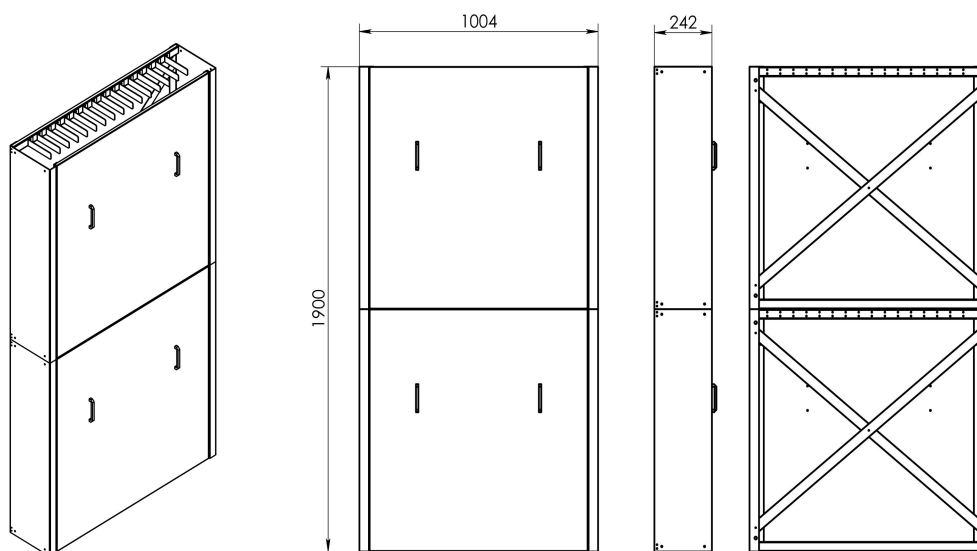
Габаритные размеры шкафа ШКП-70
